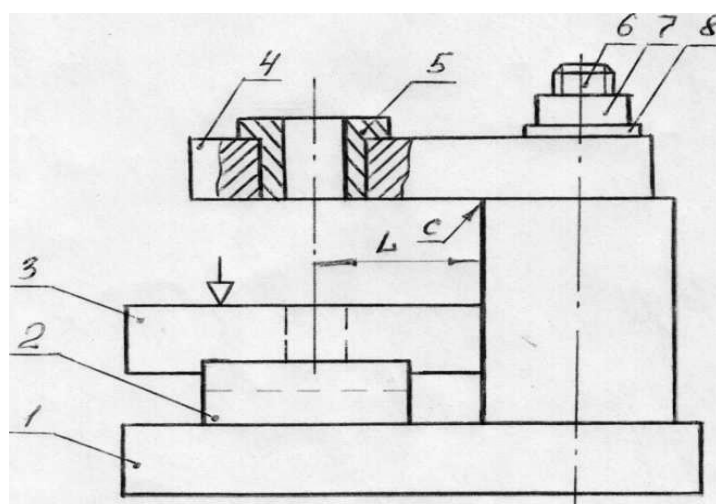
Монтажная схема приспособления: 1 - плита прямоугольная; 2 - призма; 3 - заготовка; 4 - направляющая планка; 5 - быстросменная кондукторная втулка; 6 - болт; 7 - гайка; 8 – шайба.
